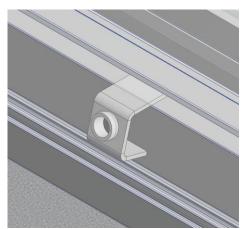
Détail d'un trou sur le cylindre d'un étrier
